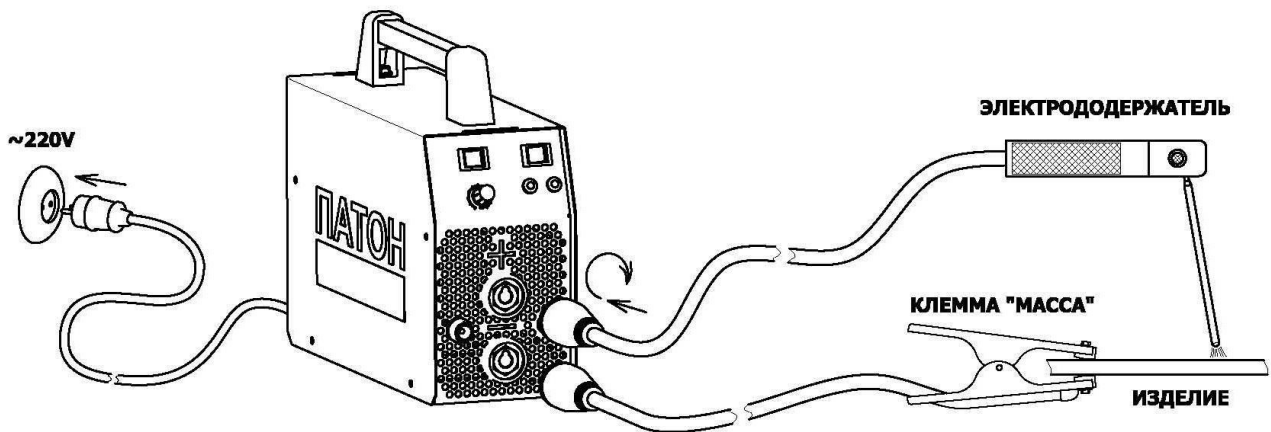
Схема подключения аппарата для сварки штучными электродами
